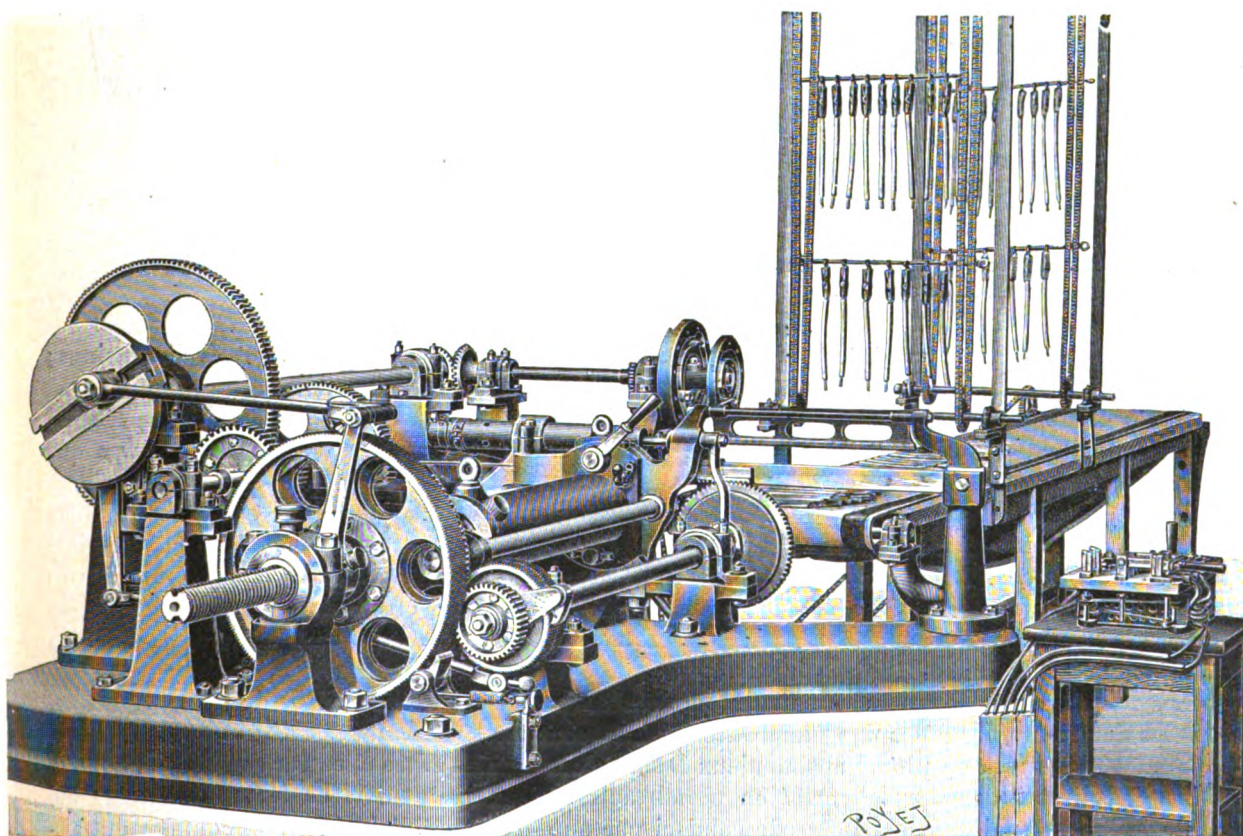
Machine à empâter et à couper les électrodes de longueur.
